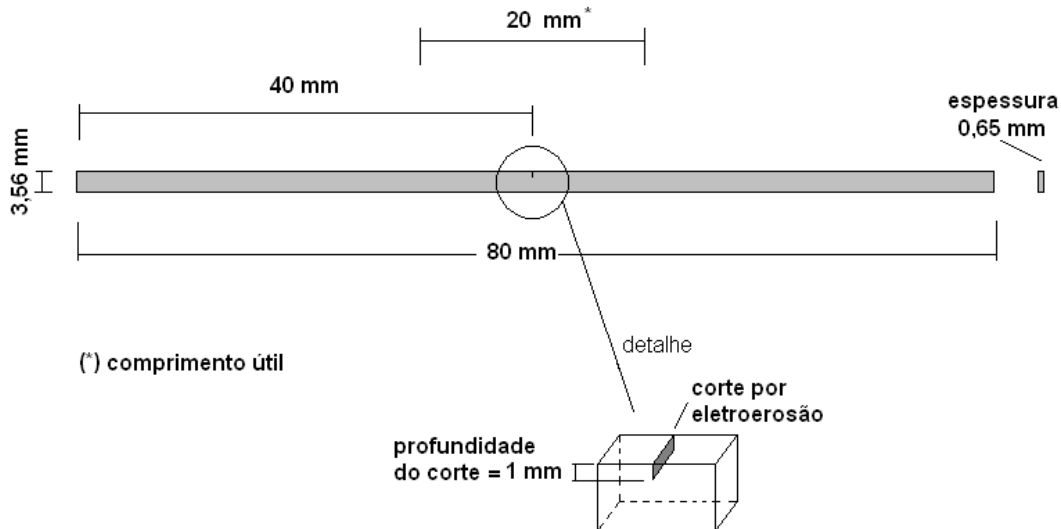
Corpo-de-prova de fratura com entalhe de 1 mm de profundidade, realizado por eletroerosão.
